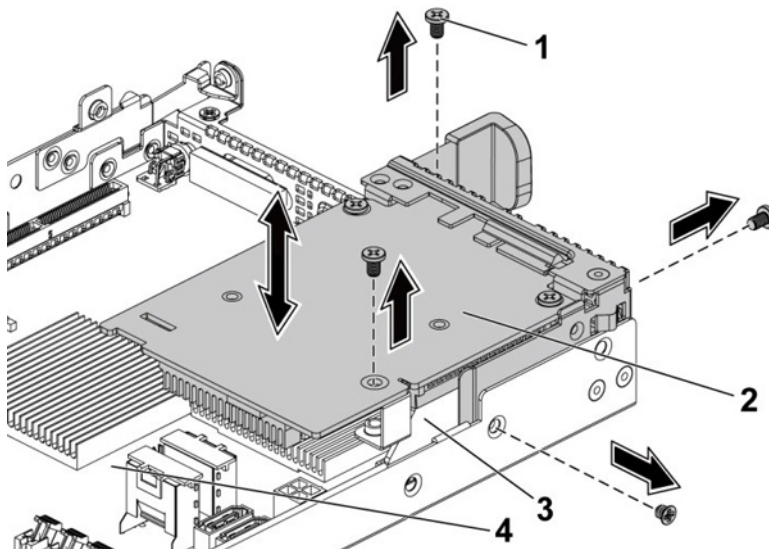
Retrait et installation de l'assemblage de carte mezzanine 1 GbE
